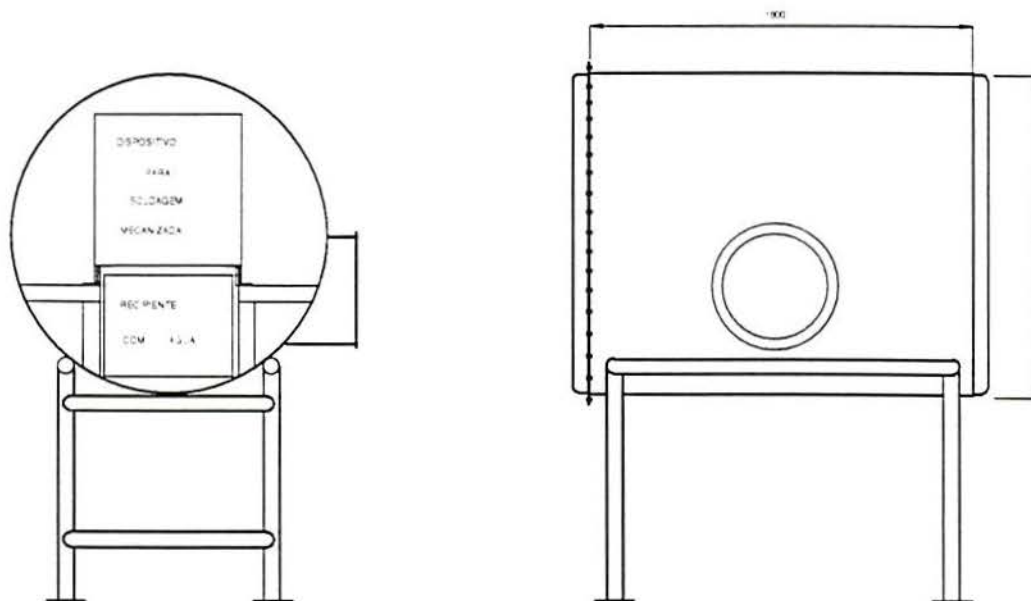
Câmara para soldagem hiperbárica, dimensões principais.
